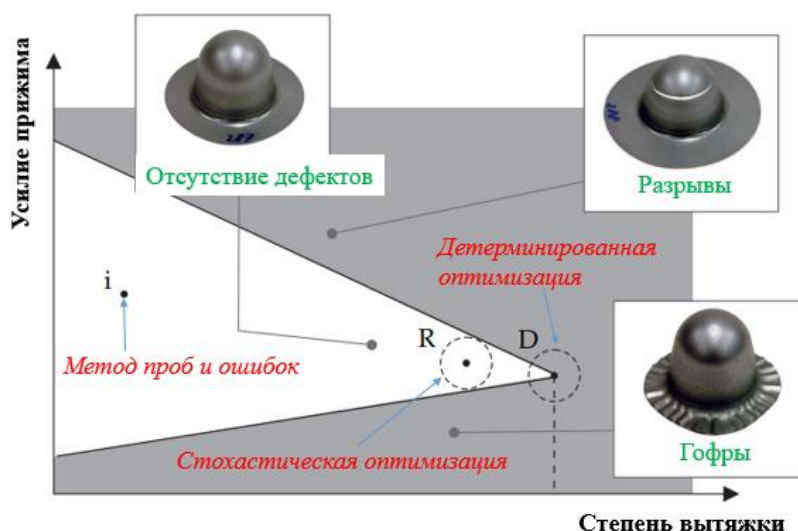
Оптимальные решения в процессе глубокой вытяжки [2]
